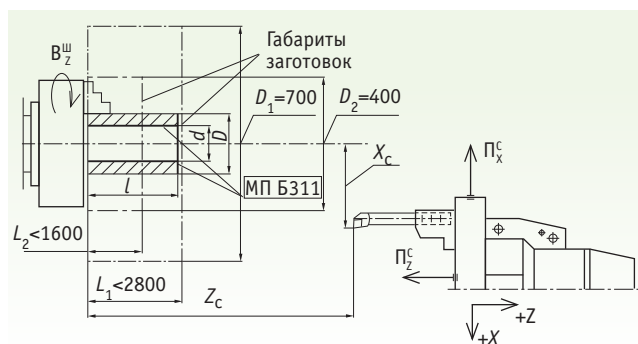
Схема рабочего пространства токарного станка 16Р35Ф3 при изготовлении МП Б311
